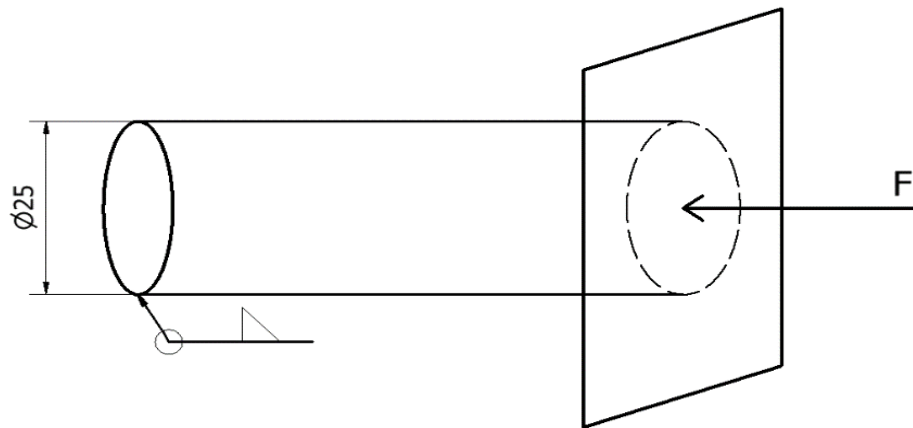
Localización de la soldadura en la barra impactora
